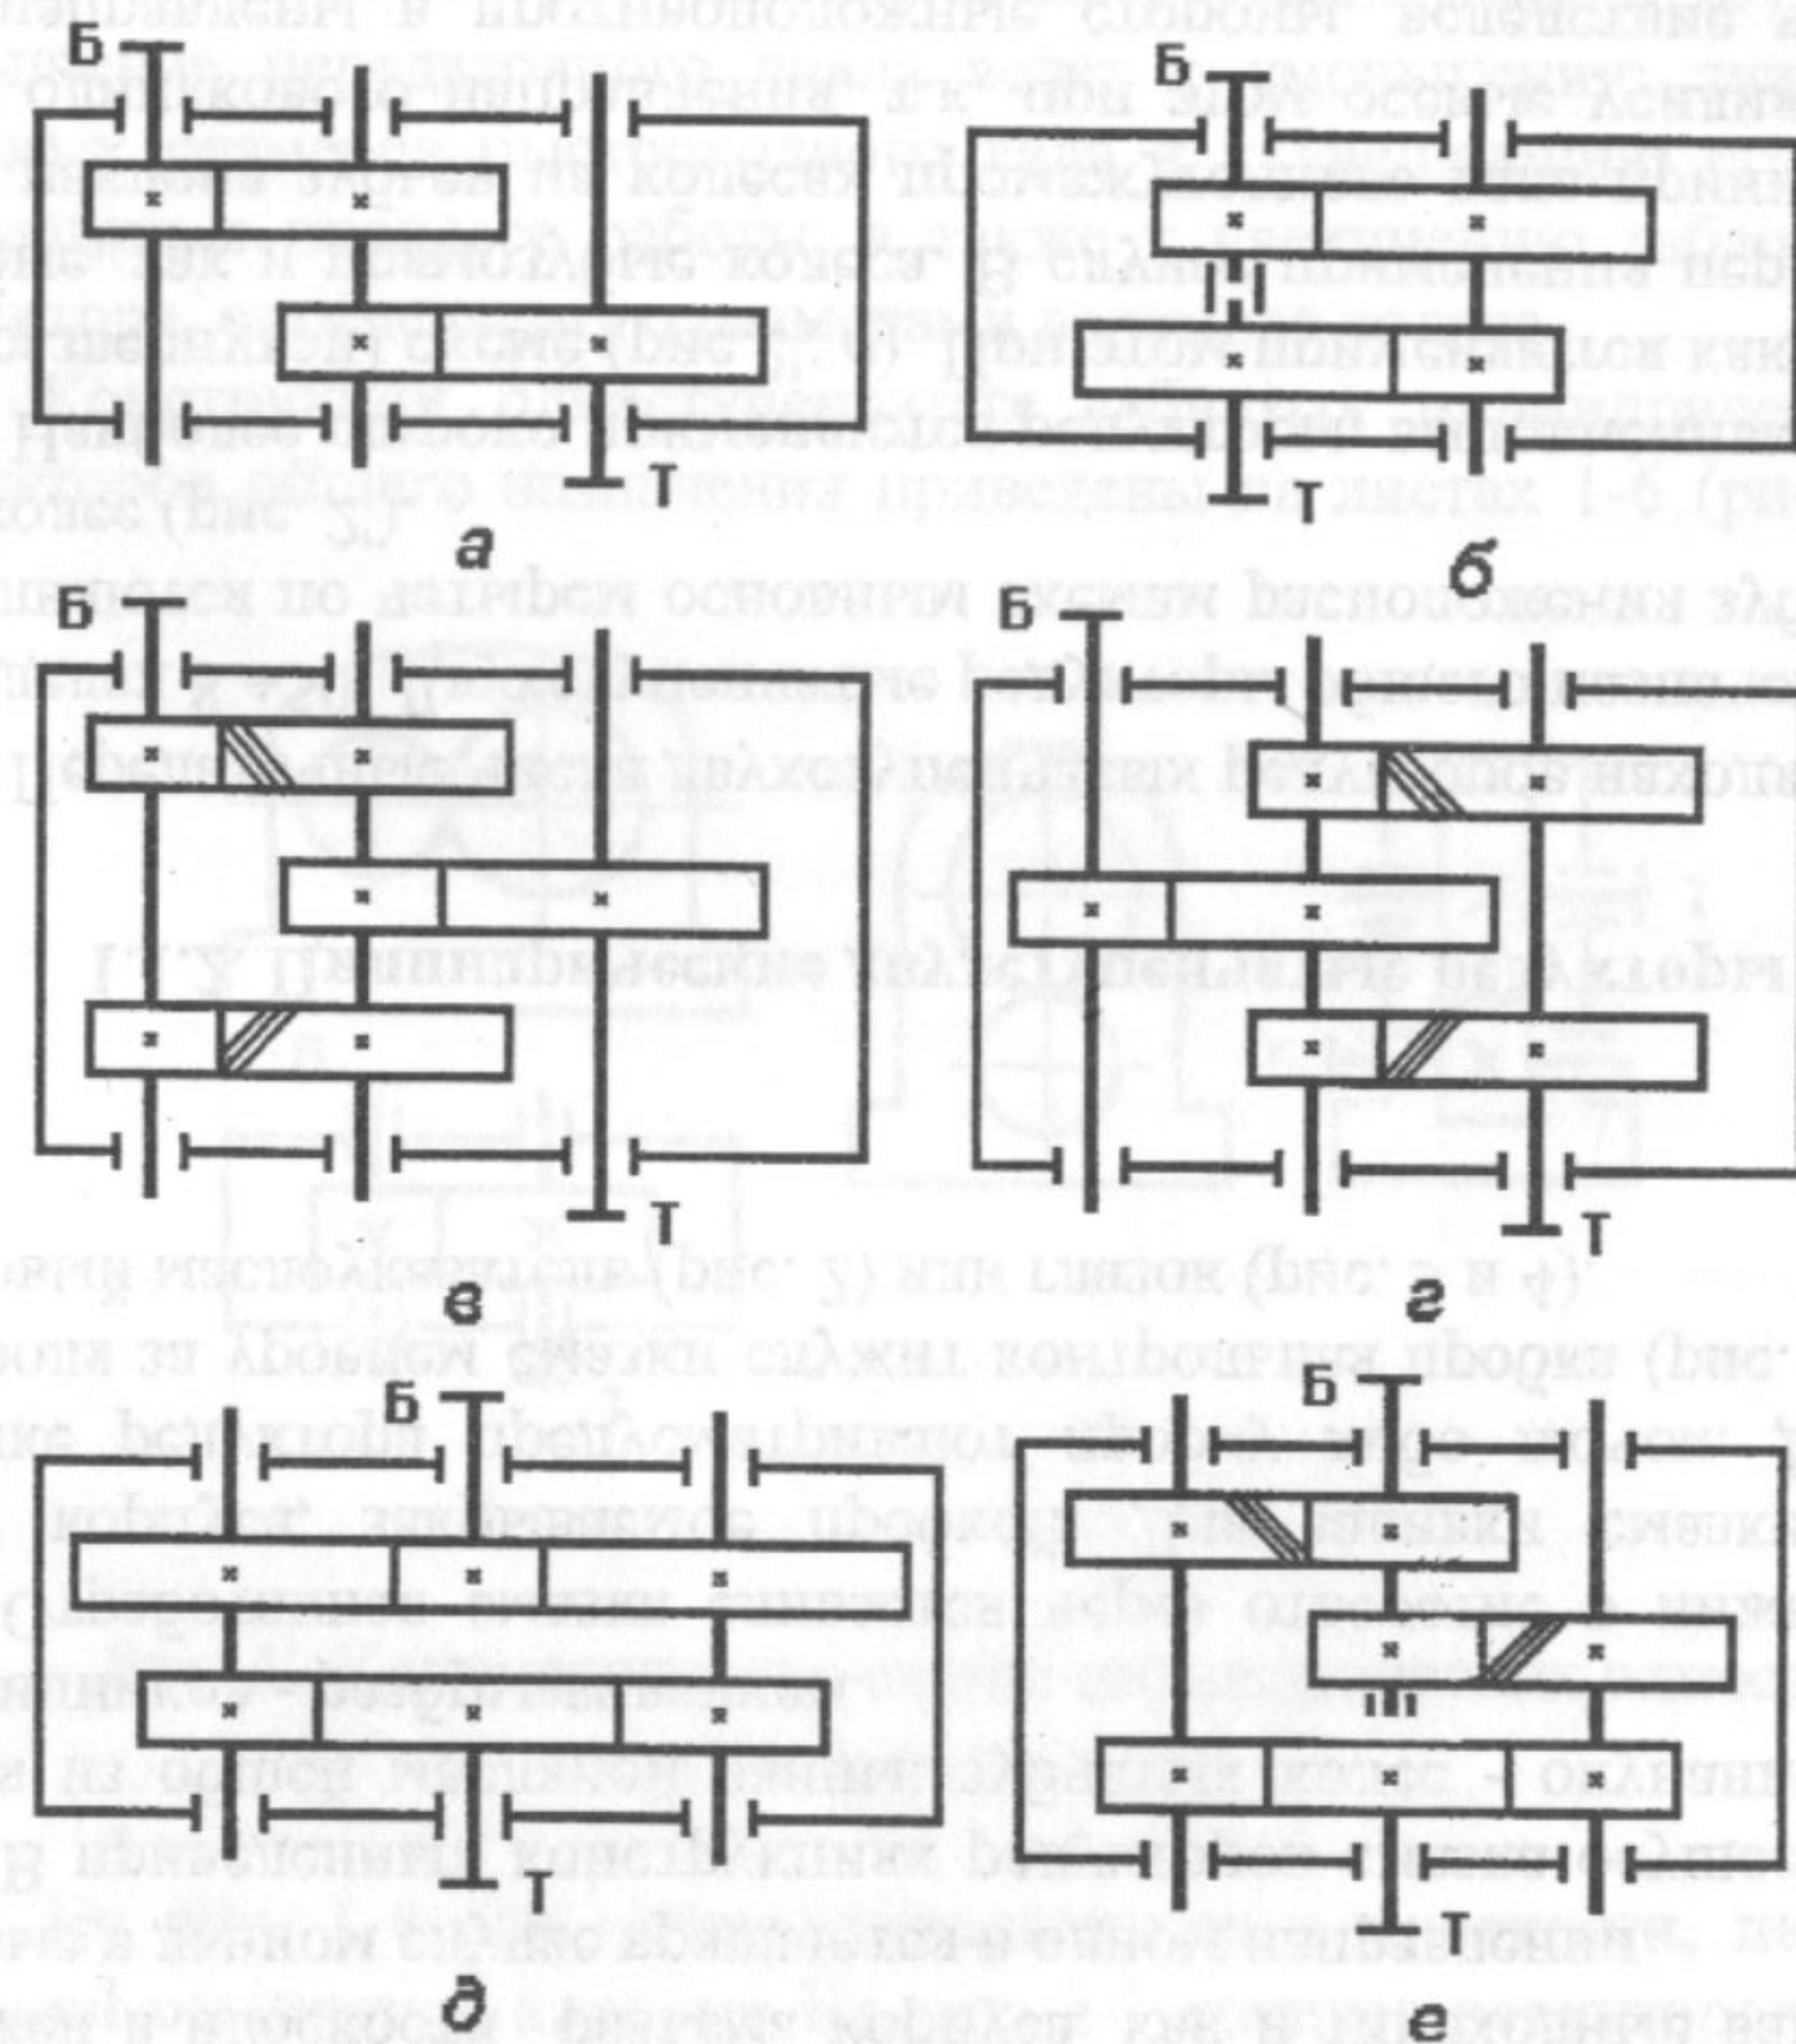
'. Кинематические схемы цилиндрических двухступенчатых редукторов
